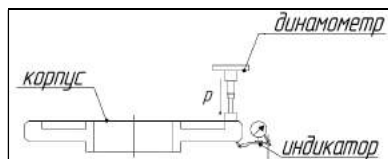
Схема исследования жесткости корпуса фрезы
